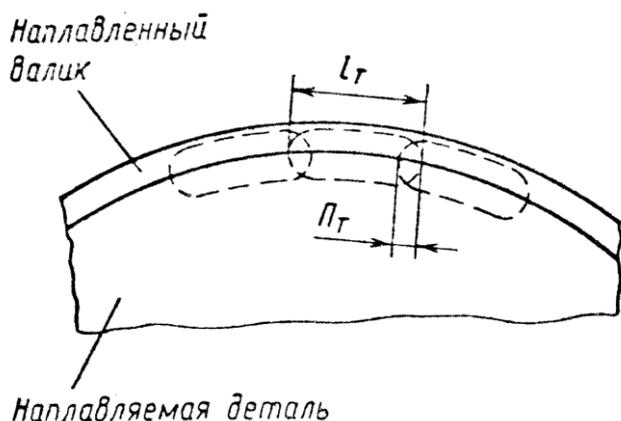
Перекрытие сварочных точек при наплавке:
